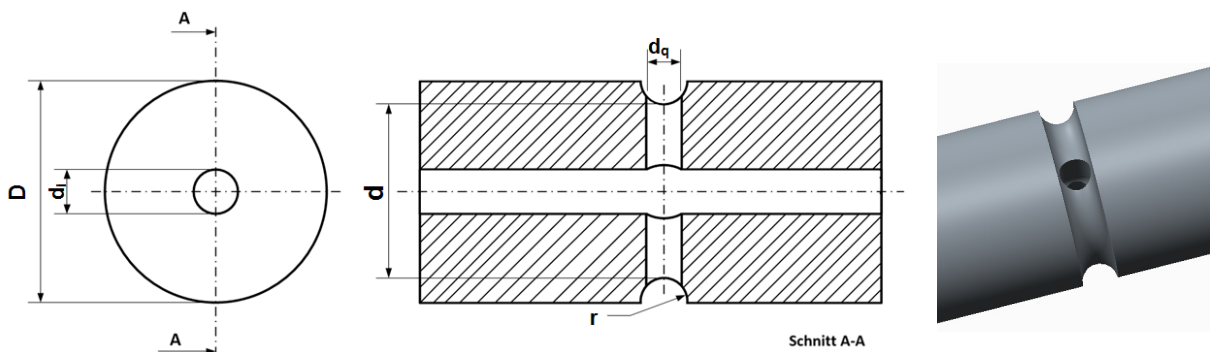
Bezeichnungen der Kerbform WmUQ (Welle mit Umlaufnut & Querbohrung)
